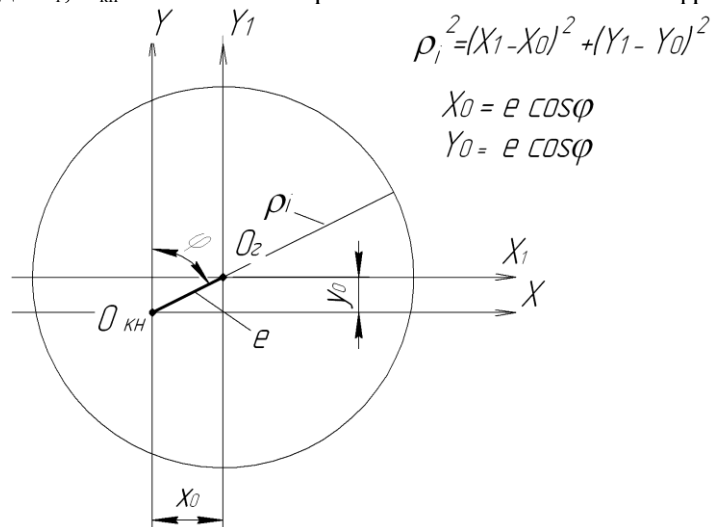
Миттєвий радіус-вектор i -го зубця дискової фрези відносно базової системи координат XO_kY
